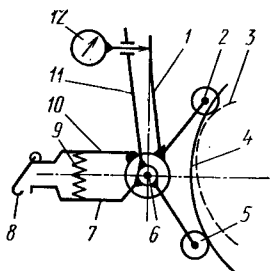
Приспособление для контроля рабочих поверхностей ремизных кулаков
